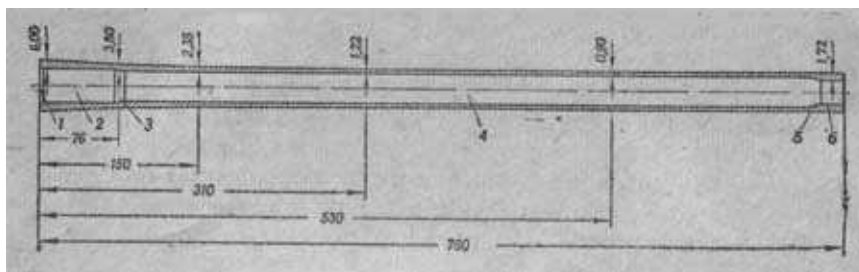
Типичная конструкция и размеры стенок ствола современного дробового двуствольного ружья: 1 - выемка под шляпку гильзы; 2 - патронник; 3 - снарядный вход (скат из патронника в ствол - переходный конус); 4 - канал ствола; 5 - чоковое сужение; 6 - канал чока
